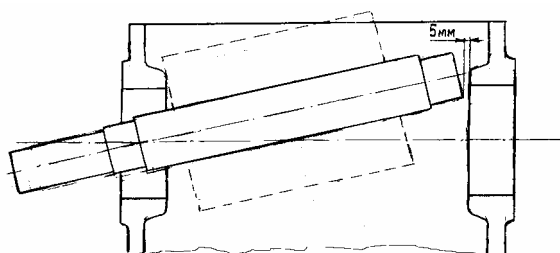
Установка вала в корпус в сборе через люк-разъем с крышкой
